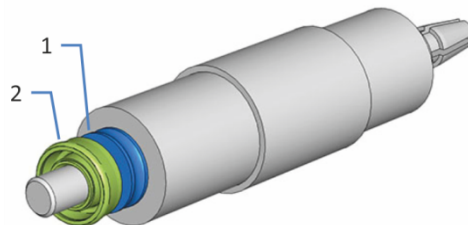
Stützring und Kolbendichtung auf dem Einbaupin für die Dichtung
